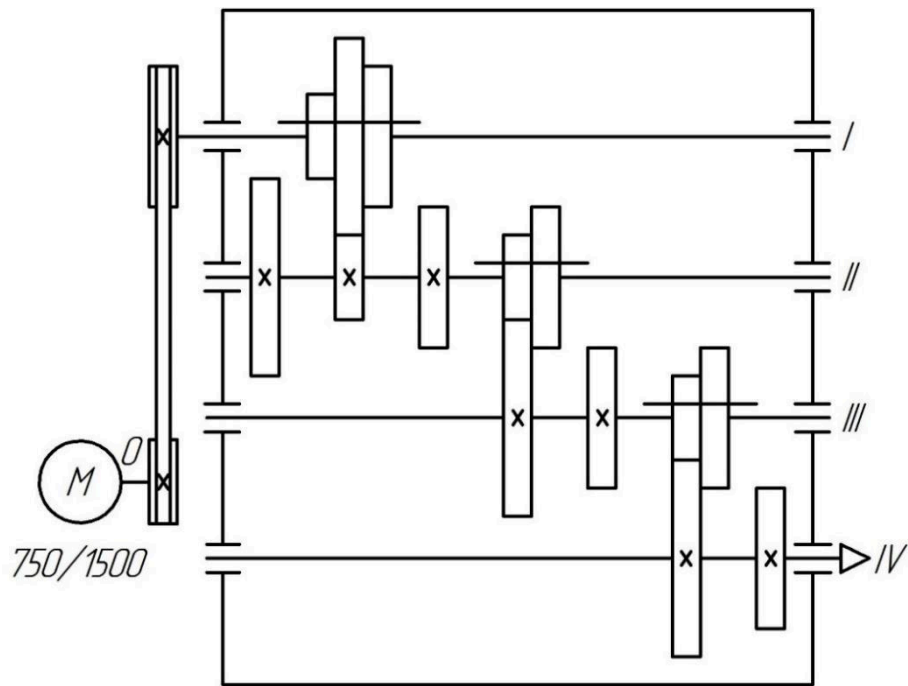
Кінематична схема коробки швидкостей для формули
